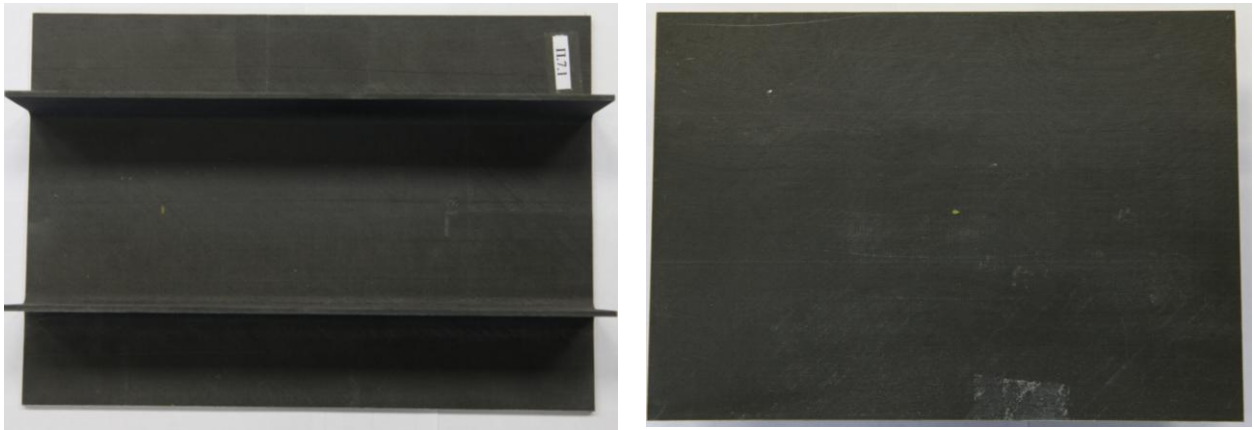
Схема конструктивно-подобного двустрингерного образца
